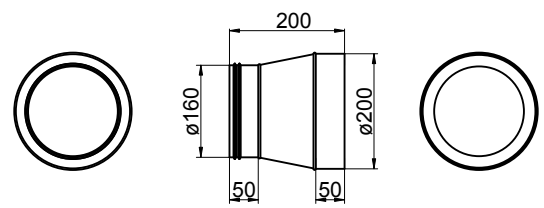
Dimensions de raccord de transition DN160 (dimensions en mm)
